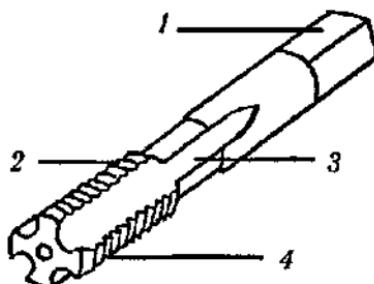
Метчик: 1 — квадратный конец хвостовика (привод); 2 — режущая резьба; 3 — паз для отвода стружки; 4 — заборная часть.
